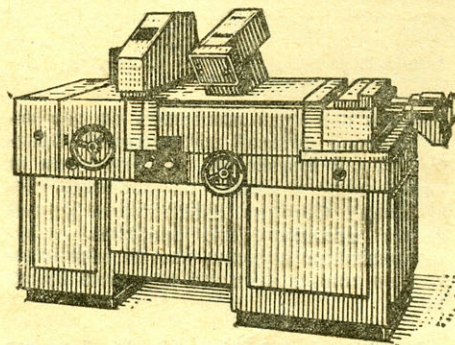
Установка для сварки дугой, вращающейся в магнитном поле.
